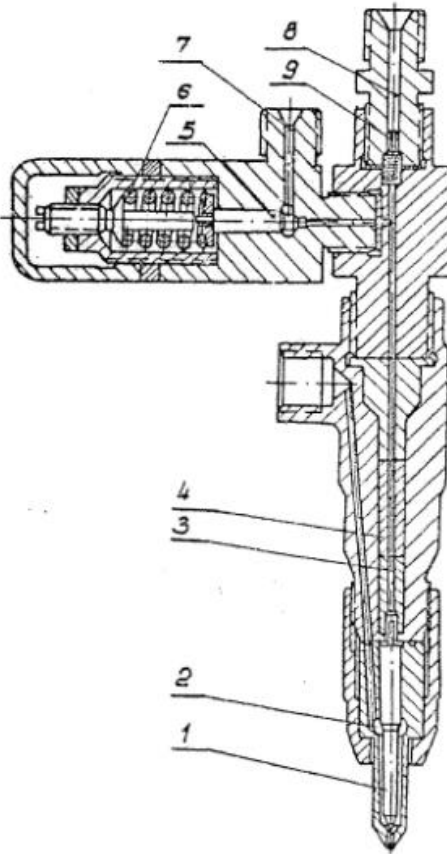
Гідрокерована форсунка з регульованим законом подачі палива: 1 - голка форсунки; 2 - підголчаста порожнина; 3 - канал підведення керуючої рідини до голки; 4 - втулки; 5 - перепускний клапан; 6 - пружина; 7 - канал перепускання керуючої рідини у бачок; 8 - канал підведення керуючої рідини до форсунки; 9 - зворотній клапан
